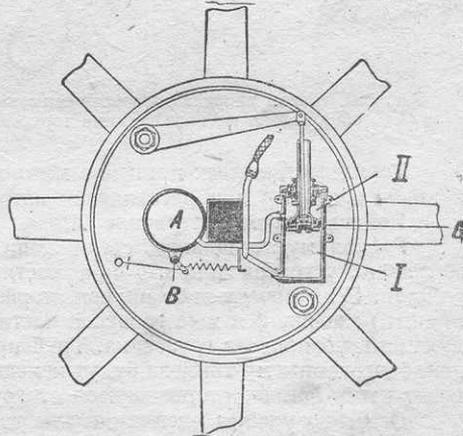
Двухкамерный тормозной цилиндр пневматических тормозов «Кнорра».
